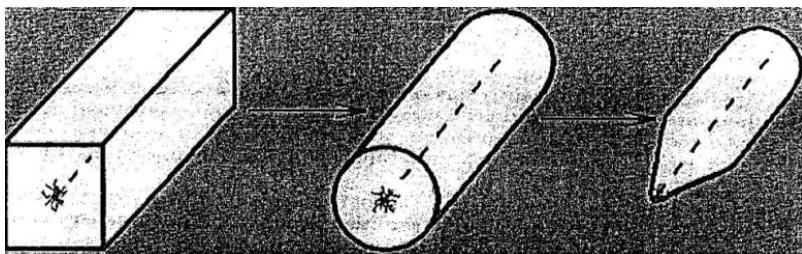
Технологическая схема изготовления прошивных оправок из поковок
